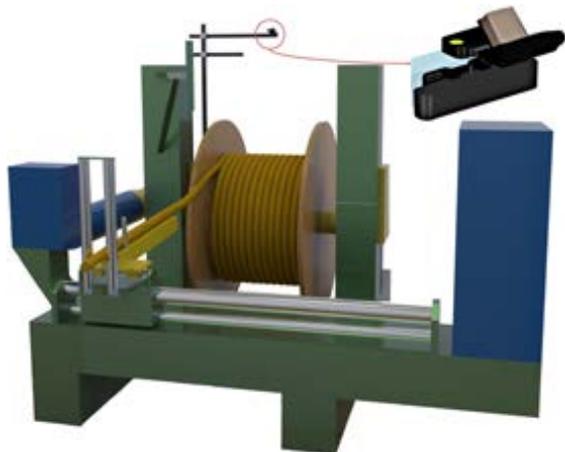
CAD Zeichnung des Kabelwickler mit Detailsicht
